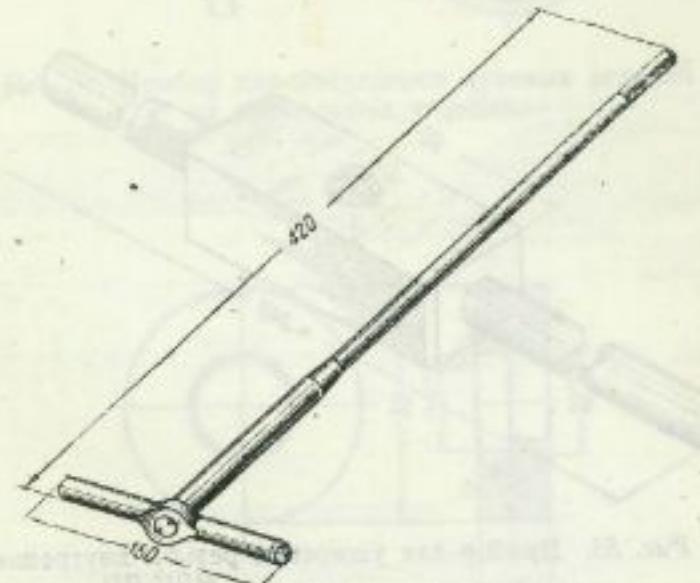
Вороток Д-ПП ПМ-30 для конической развёртки Д-И ПМ-11.
